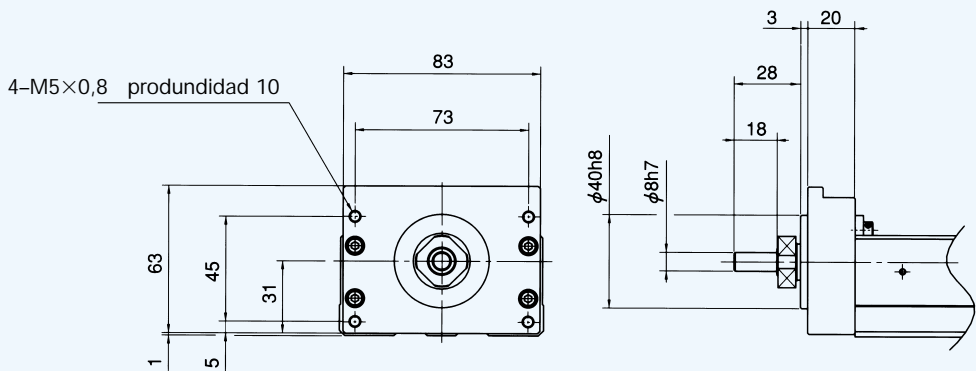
■ KR46 Adaptador A sin brida de motor (indicativo 50).
